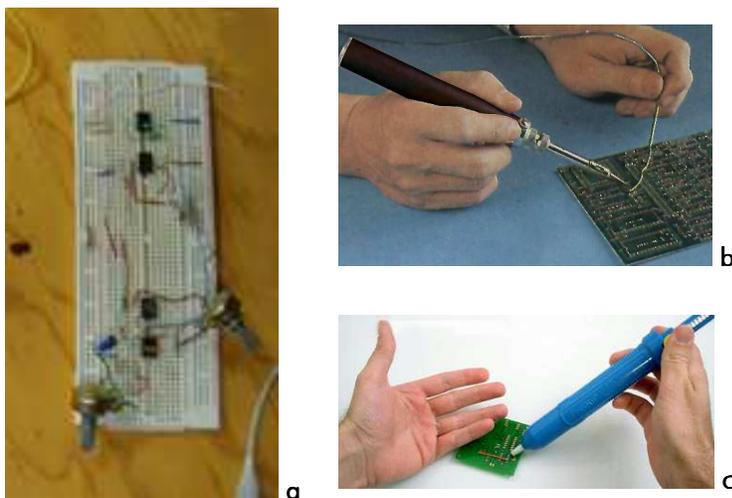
Tarjeta de prueba (a), aplicación de soldadura (b) y extracción de soldadura (c).
